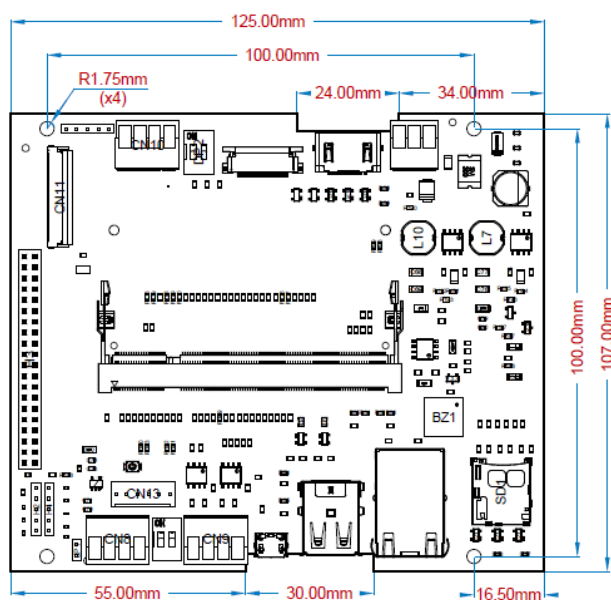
Dimensões mecânicas CPU SoM (PR17037)
